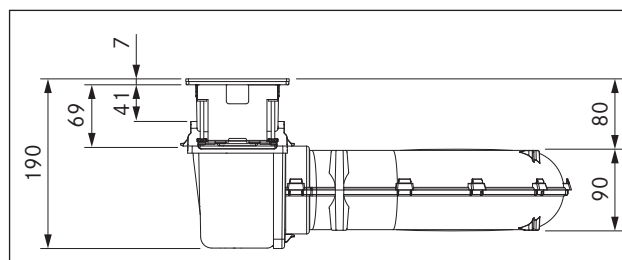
Dimensões do aparelho CKA2, vista frontal
